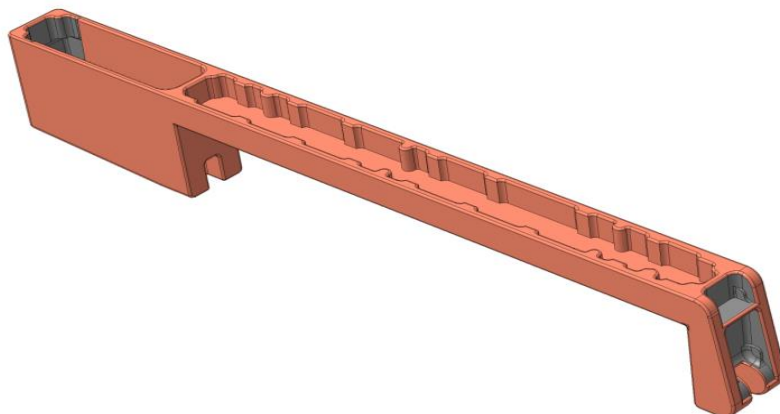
Комп'ютерна модель заготовки деталі «Балка»
